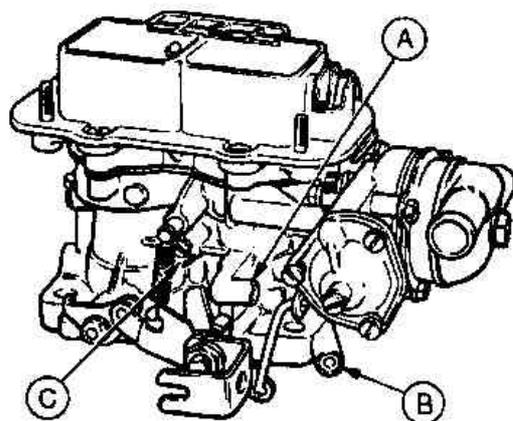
Точки регулировки малых оборотов карбюратора "Вебер" (Разд.18)
